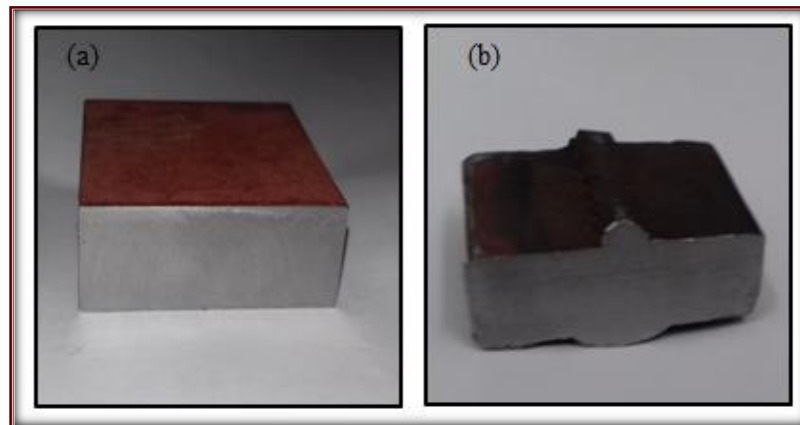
Photo des échantillons fournis : (a) sans soudure ; (b) avec soudure.
